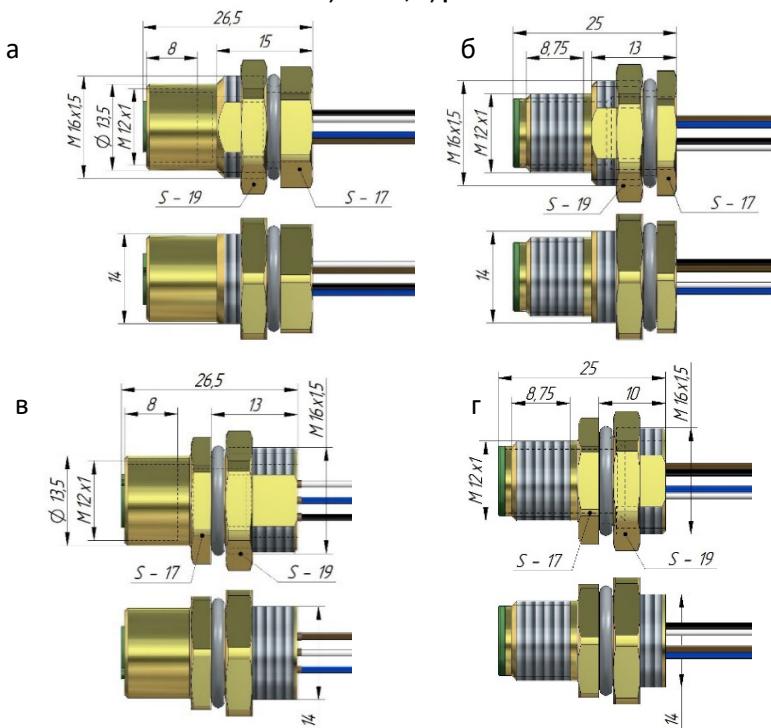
Внешний вид и габаритные размеры блочных разъемов:
